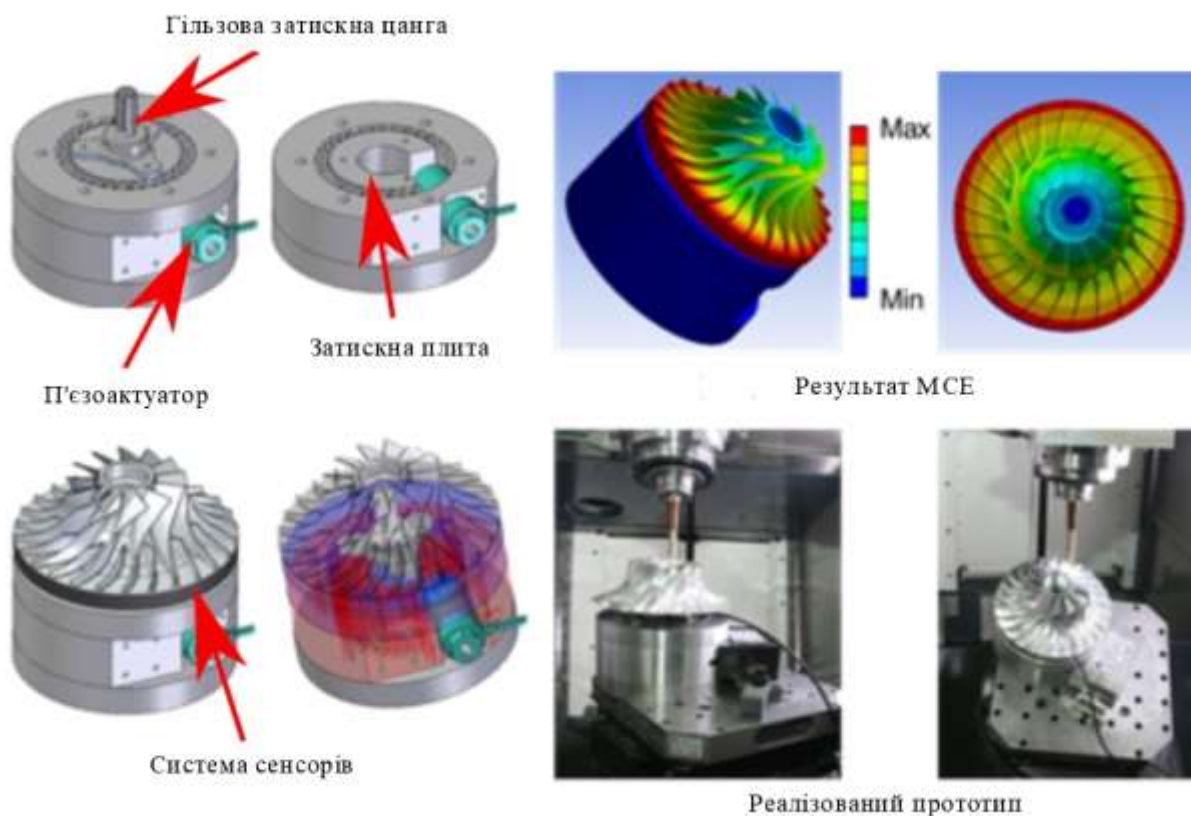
Остаточна концепція механічної конструкції обертального пристрою
